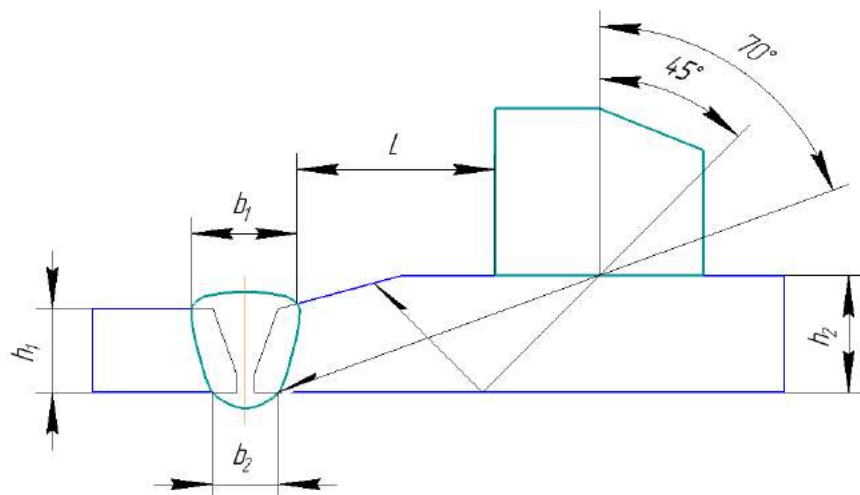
Схема прозвучивания сварного шва № 1 ФР прямым и однократно отраженным лучами
